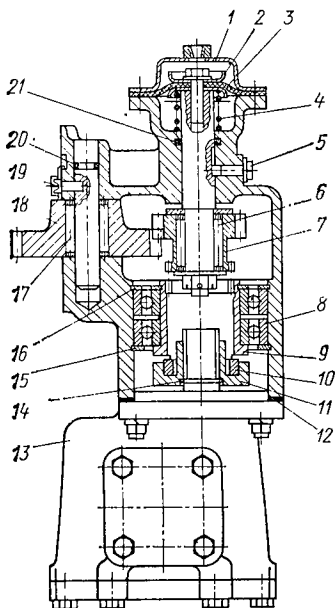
Коробка отбора мощности: 1 — крышка; 2 — шайба; 3 — диафрагма; 4 — пружина; 5 — установочный винт; 6, 8 и 17 — подшипники; 7 — ведущая шестерня; 9 — зубчатая полумуфта; 10 — призма; 11 — муфта; 12 — прокладки; 13 — насос; 14, 15 и 16 — стопорные кольца; 18 — промежуточная шестерня; 19 — болт; 20 и 21 — уплотнительные кольца
